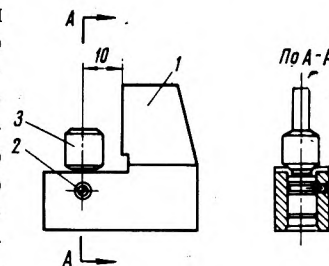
Калибр для проверки отверстий под шканти в боковине:
